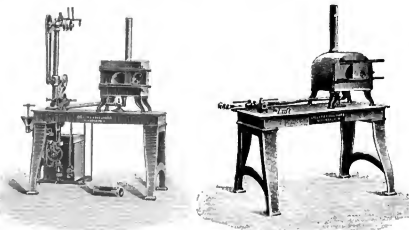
Fig. 49. Härteöfen mit Gasgebläse von Collet & Engelhard, Offenbach a. M.
